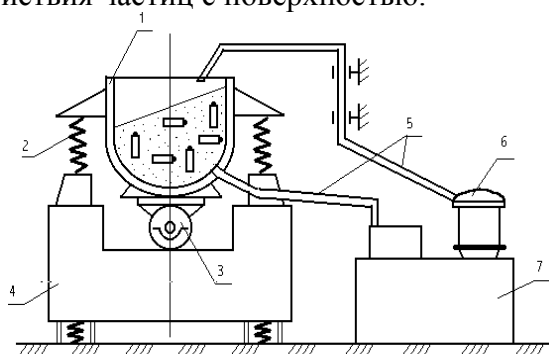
Схема процесса виброударной обработки: 1 - рабочая камера; 2 - пружины; 3 - дебалансный вибратор; 4 - основание; 5 - шланги для подачи и слива ТЖ; 6 - помпа; 7 - бак-отстойник.
